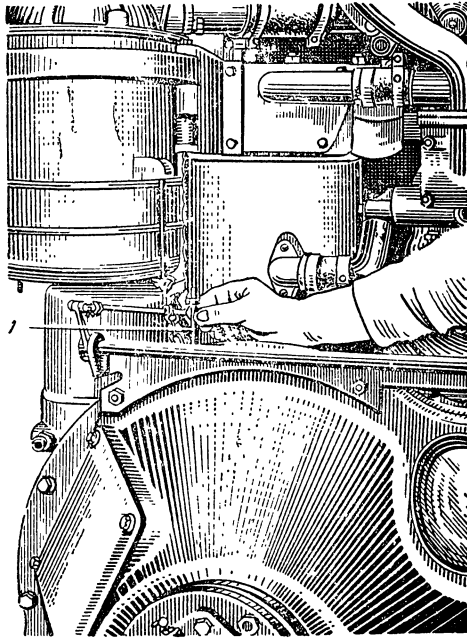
Установка поршня первого цилиндра в верхнюю мертвую точку по углублению в маховике:
